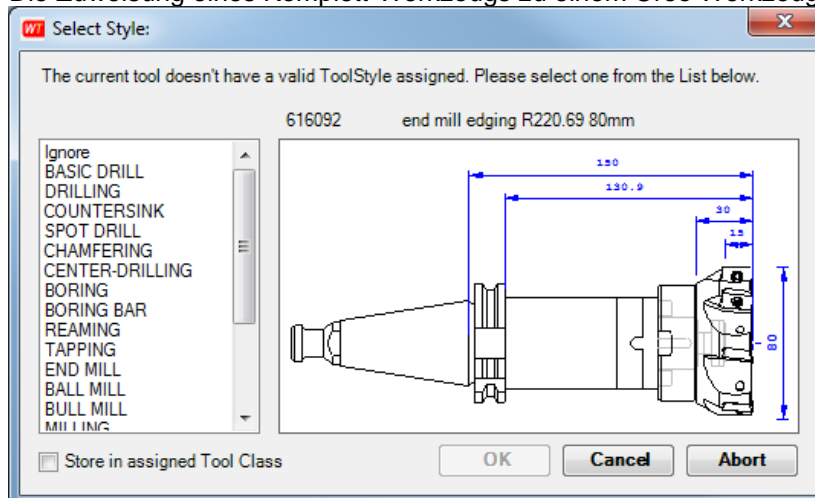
Zuweisung Komplett-Werkzeug zu Creo Werkzeugtyp
